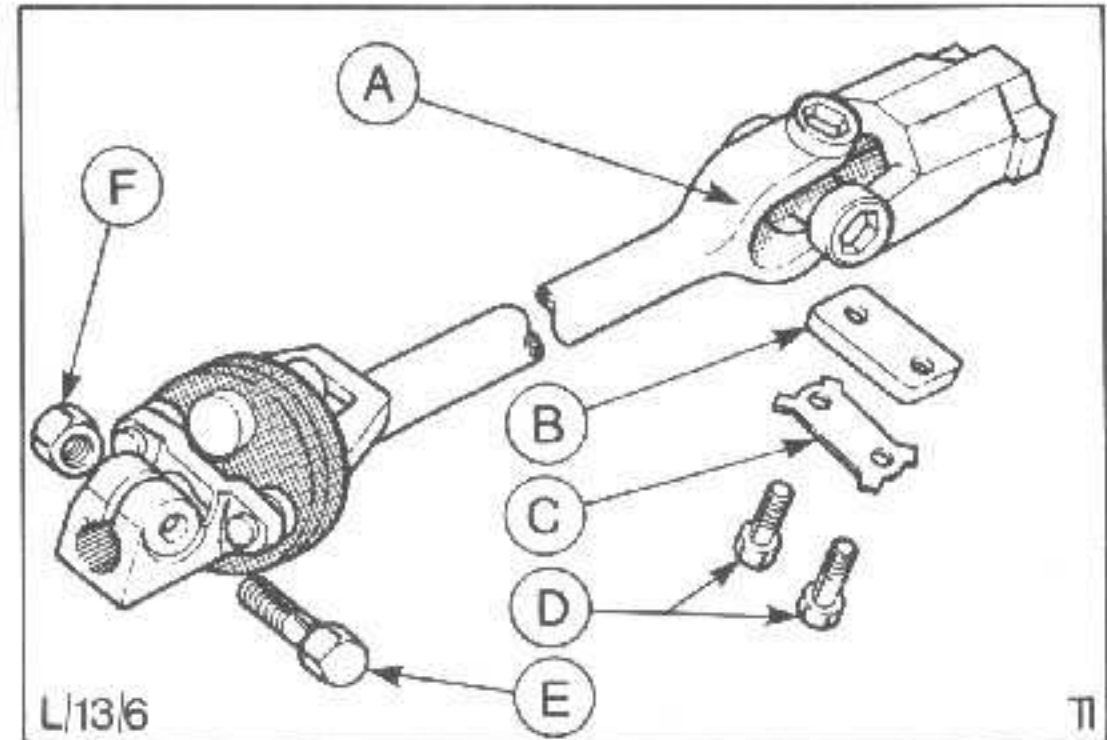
A = Universalgelenk D = Klemmschraube - Lenkspindel
